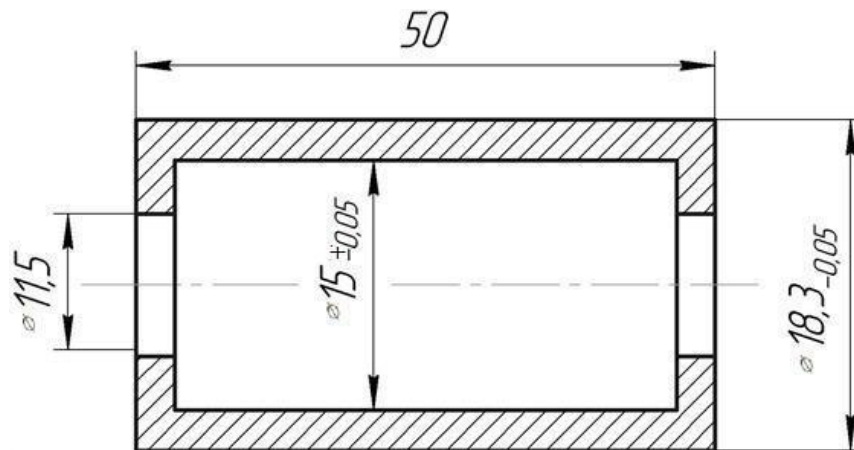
Сталева втулка для пружинного конічного вкладиша
